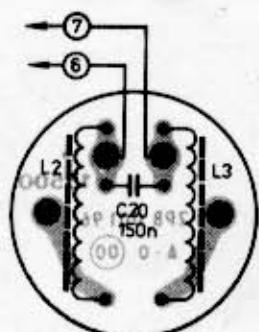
Deska pojistek pájená (pohled ze strany spojů)
